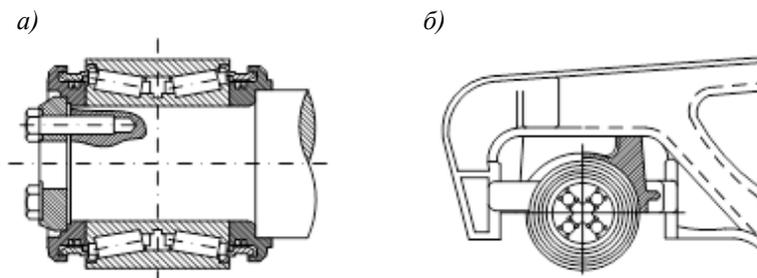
Буксовый узел с подшипниками кассетного типа
